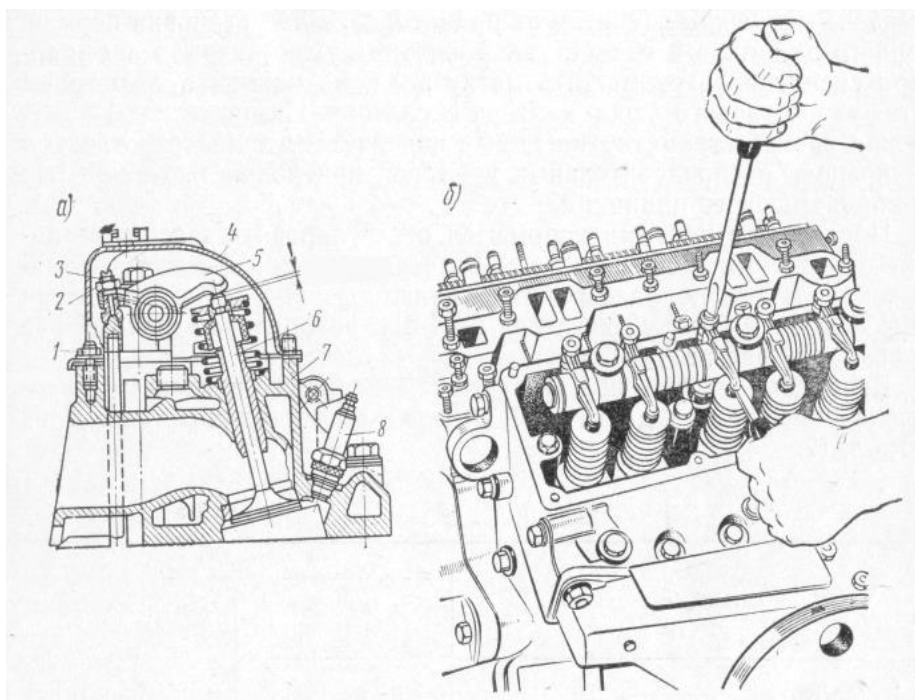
Регулировка теплового зазора в клапанном механизме двигателя ЗИЛ-508.10: а – разрез головки цилиндров, б – регулировка зазора;
